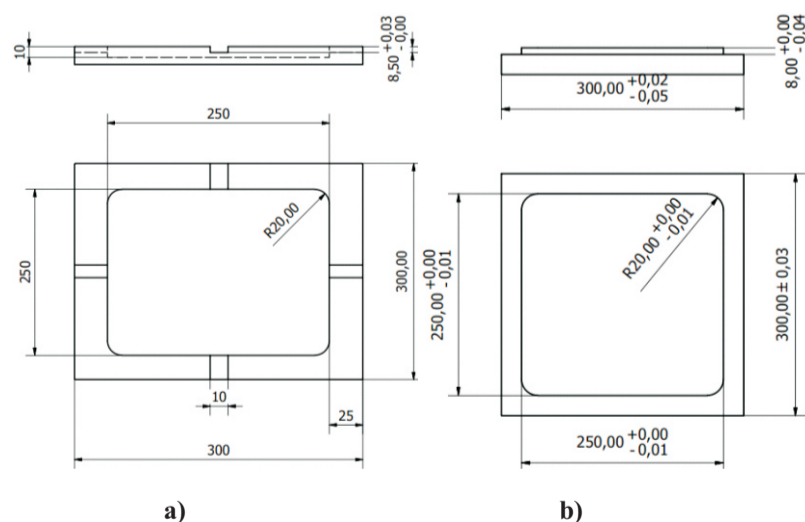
Diseño del molde, a) Cavidad del molde, b) Macho
